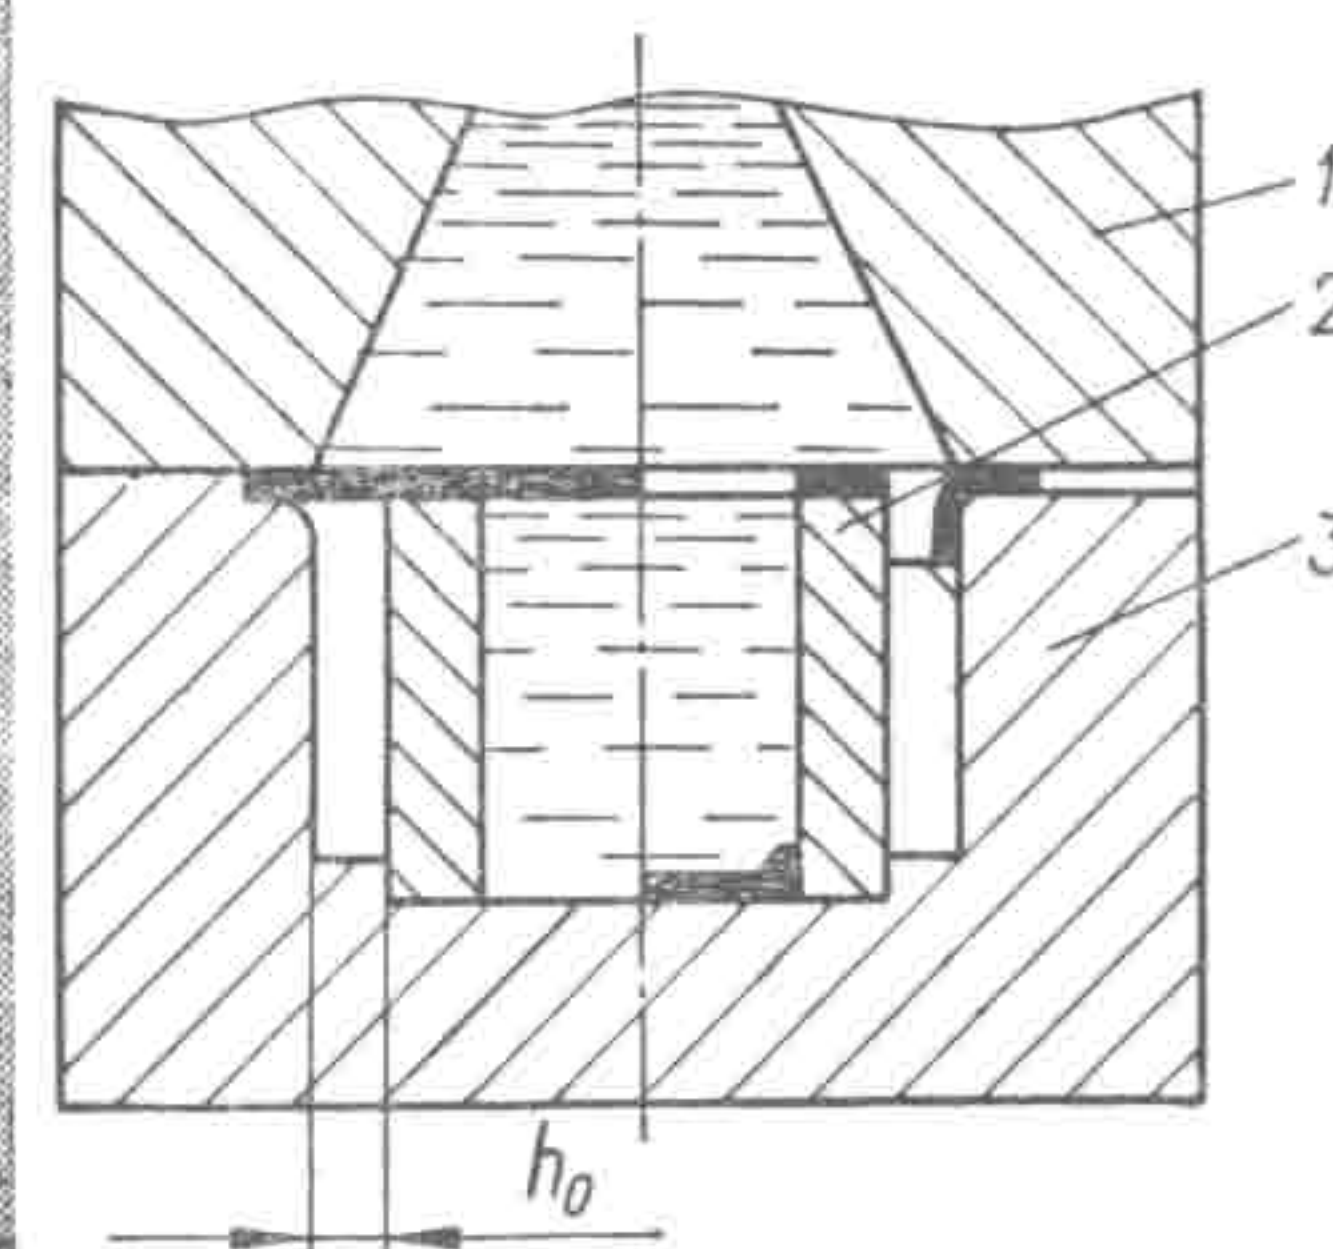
Типовая схема оснастки для пробивки — вырубki.
